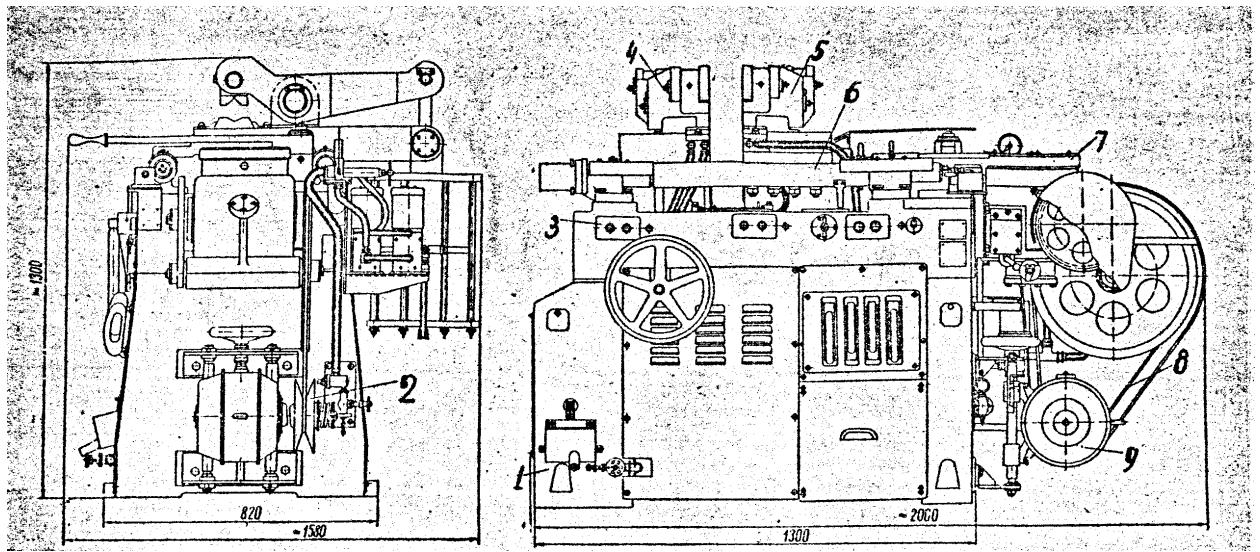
Общий вид машиныстыковой сварки:
